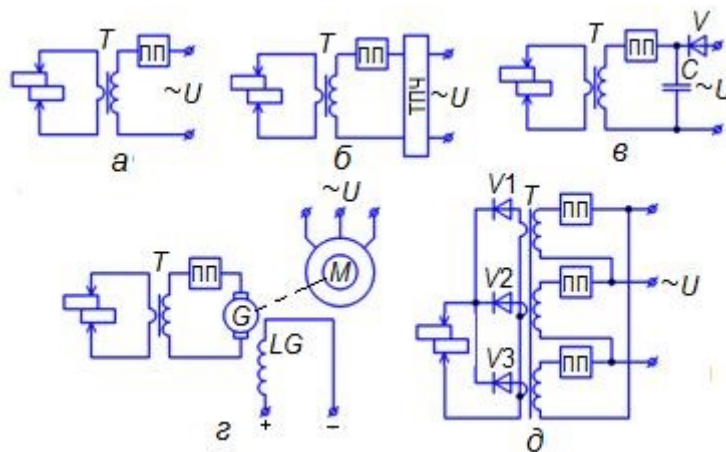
Електричні схеми зварювальних установок для контактного зварювання
